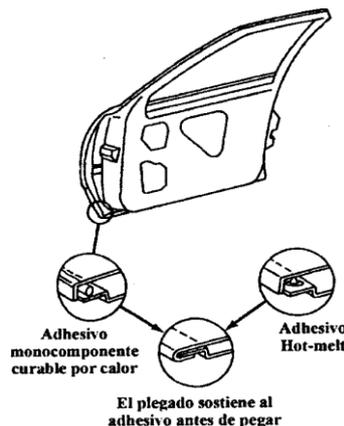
Plegado y unión con adhesivos en la puerta de un automóvil.
